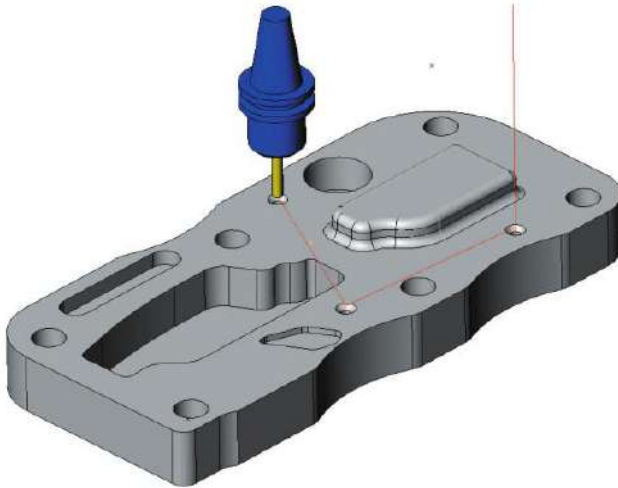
Обробка отворів: свердління (Drill), нарізання різьби (Threading), розточування (Boring); основні параметри – тип операції та глибина обробки
